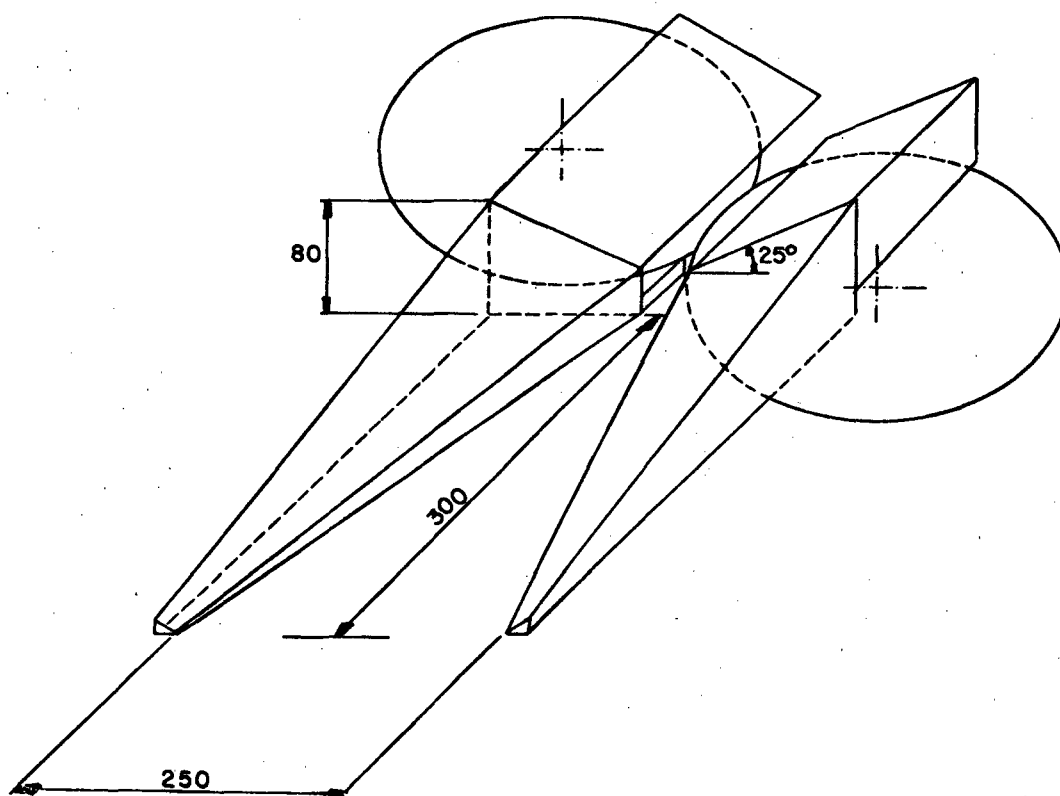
Proposta para reprojeto dos levantadores de plantas.
